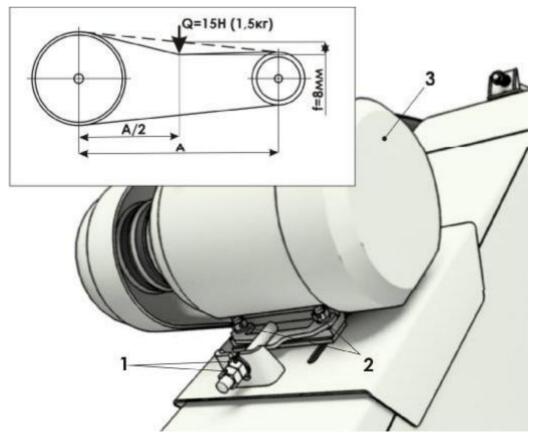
Регулировка натяжения клиноременной передачи привода загрузочного транспортера
